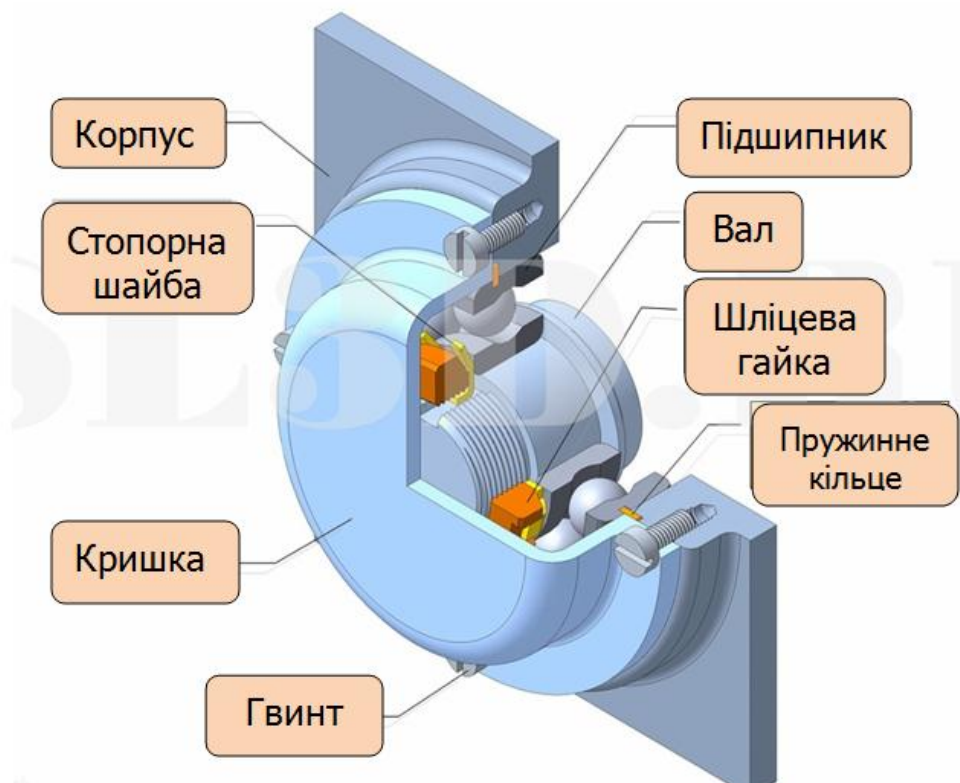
Установка підшипника з виточною за допомогою розрізного пружинного кільця
